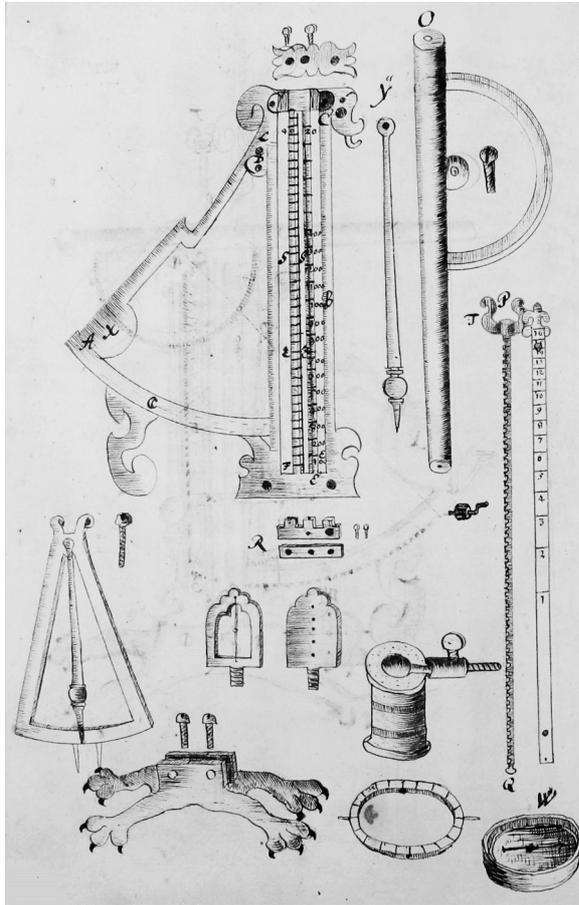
Quadrant zum Richten einer Kanone, Explosionszeichnung, in J. C. Kaukol, *Püchsenmeistery*, fol. 28<sup>v</sup> (Riksarkivet Stockholm)
